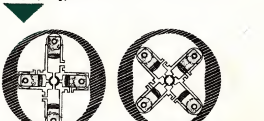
Двигатель Меркера. Крестообразный блок цилиндров, в котором ходят поршни, охватывающиеся роликами, вращается внутри корпуса со звездообразной поверхностью вокруг впускной трубы с прорезями, служащей цилиндрическим золотником. Для выпуска служат окна (двигатель работает по двухтактному циклу).
